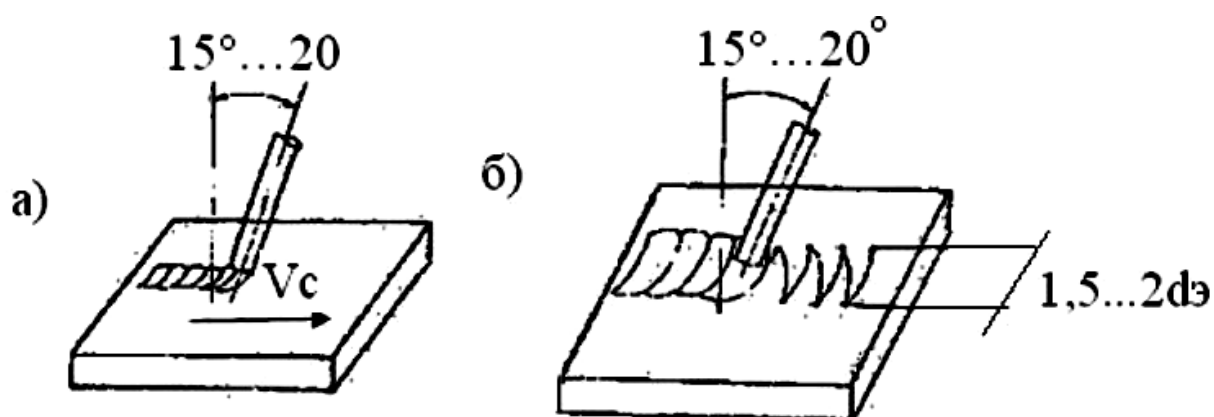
Схема ручной дуговой наплавки покрытыми штучными электродами
